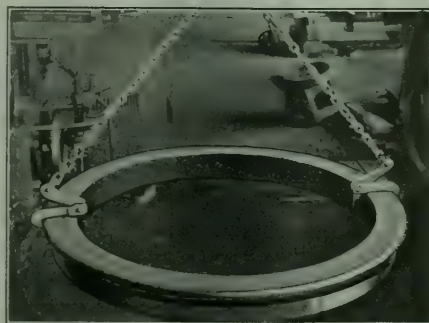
LA LLANTA SUSPENDIDA POR LOS GANCHOS
